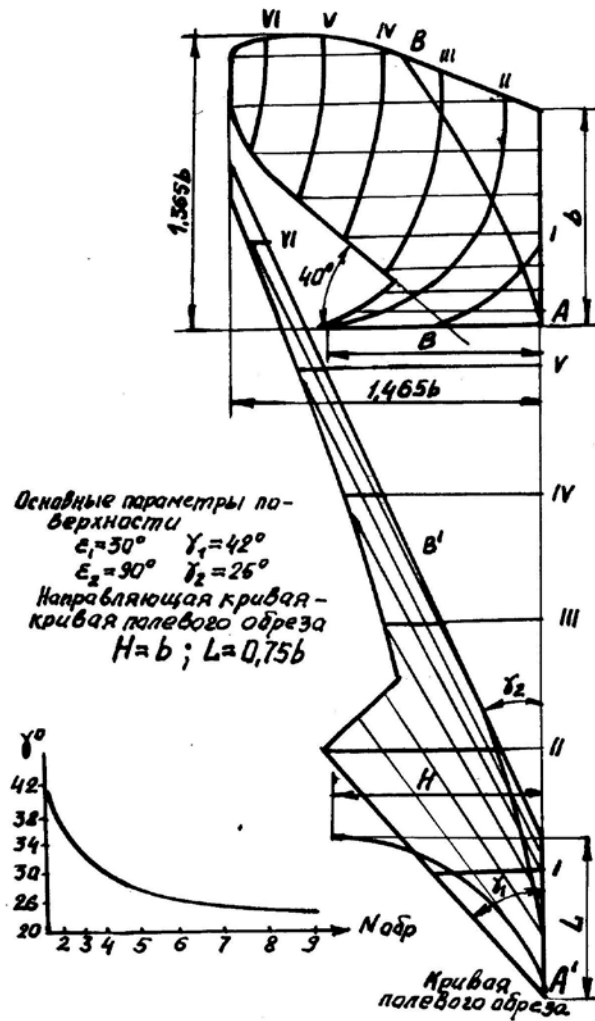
Поверхня корпусу для швидкісної оранки
